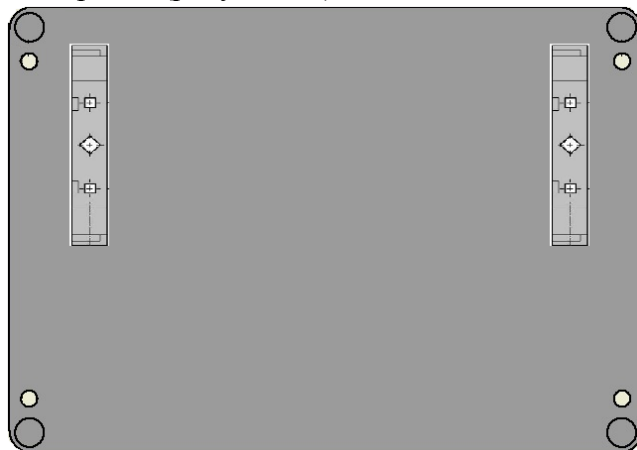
Крепление кронштейнов на задней стенке корпуса Контроллера для монтажа Контроллера на DIN-рейке
